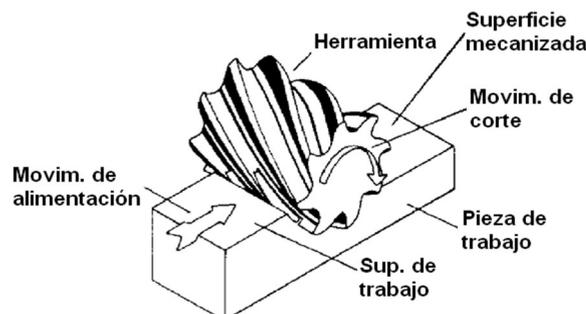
Fresado con una fresadora horizontal tipo rodilla.
